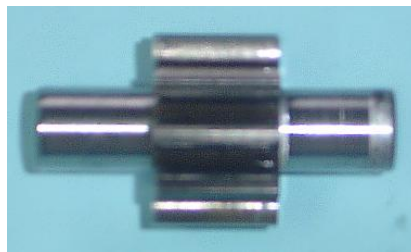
Separación de la Bomba de Engranés del cuerpo de la bomba
